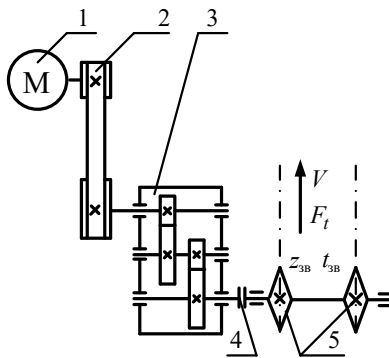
Кинематическая схема привода цепного конвейера:
